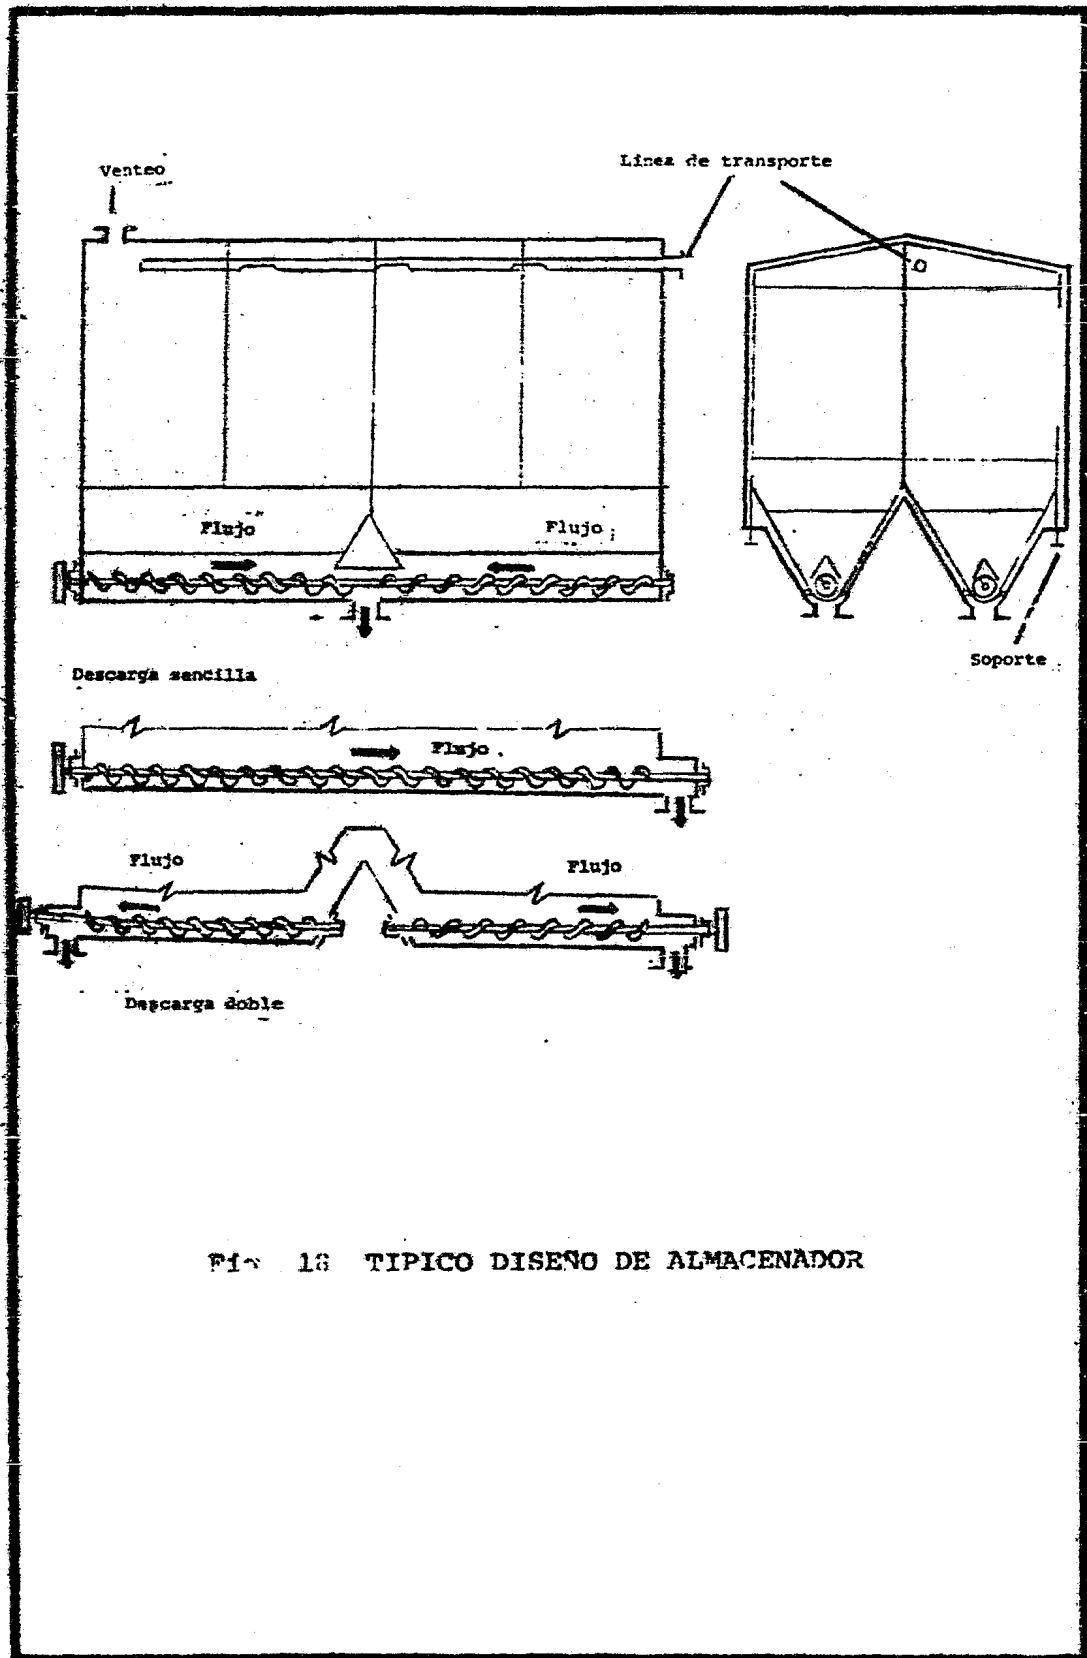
TÍPICO DISEÑO DE ALMACENADOR
